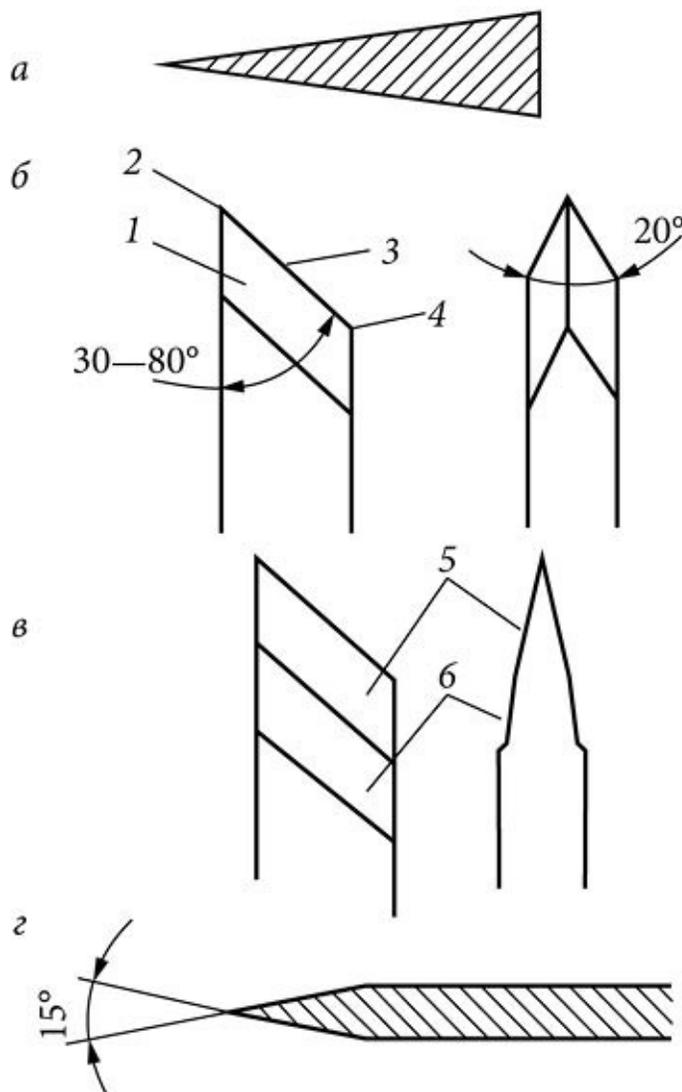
Заточка ножей: а – клиновидная форма лезвия; б – заточка косяка с одной фаской; в – заточка косяка с двойной фаской; г – правильно заточенное лезвие резака: 1 – фаска; 2 – носок; 3 – лезвие; 4 – пятка; 5 – первая фаска; 6 – вторая фаска.
